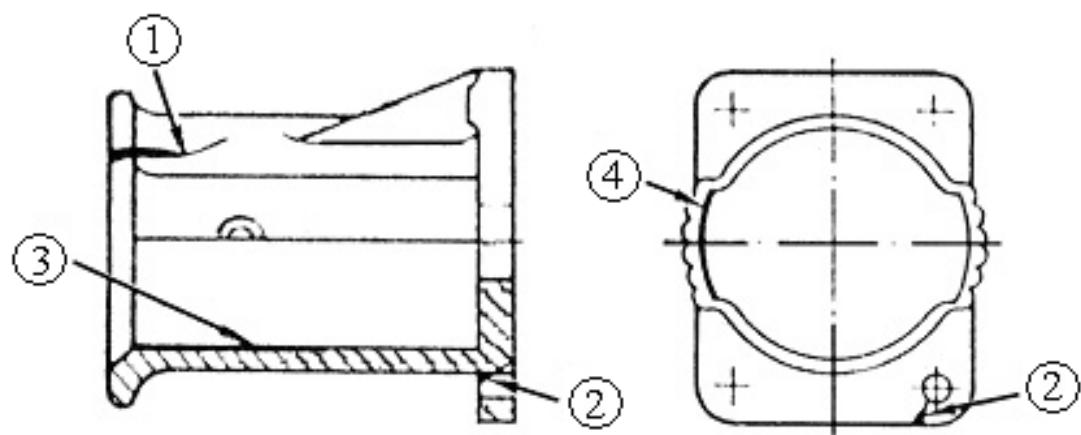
Дефекты стакана буферного, ремонтируемые сваркой или наплавкой
